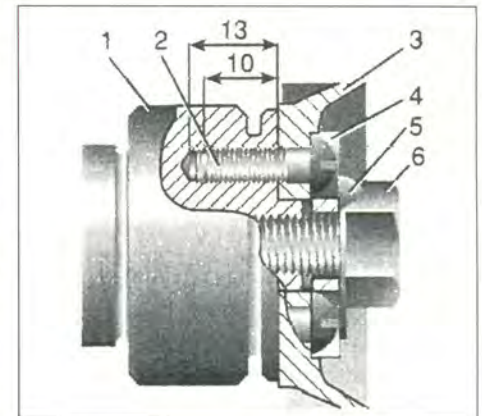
Измененная конструкция соединения распределительного вала и звездочки: 1 – распредвал; 2 – винт М6; 3 – звездочка; 4 – опорная шайба; 5 – контровочная шайба; 6 – центральный болт.
